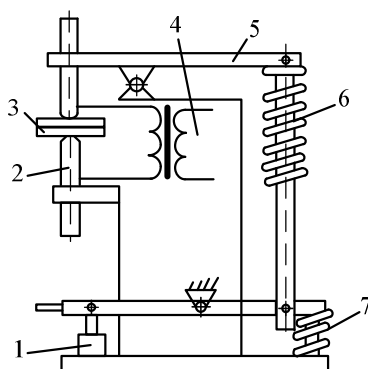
Конструктивная схема машины для электроконтактной точечной сварки:
